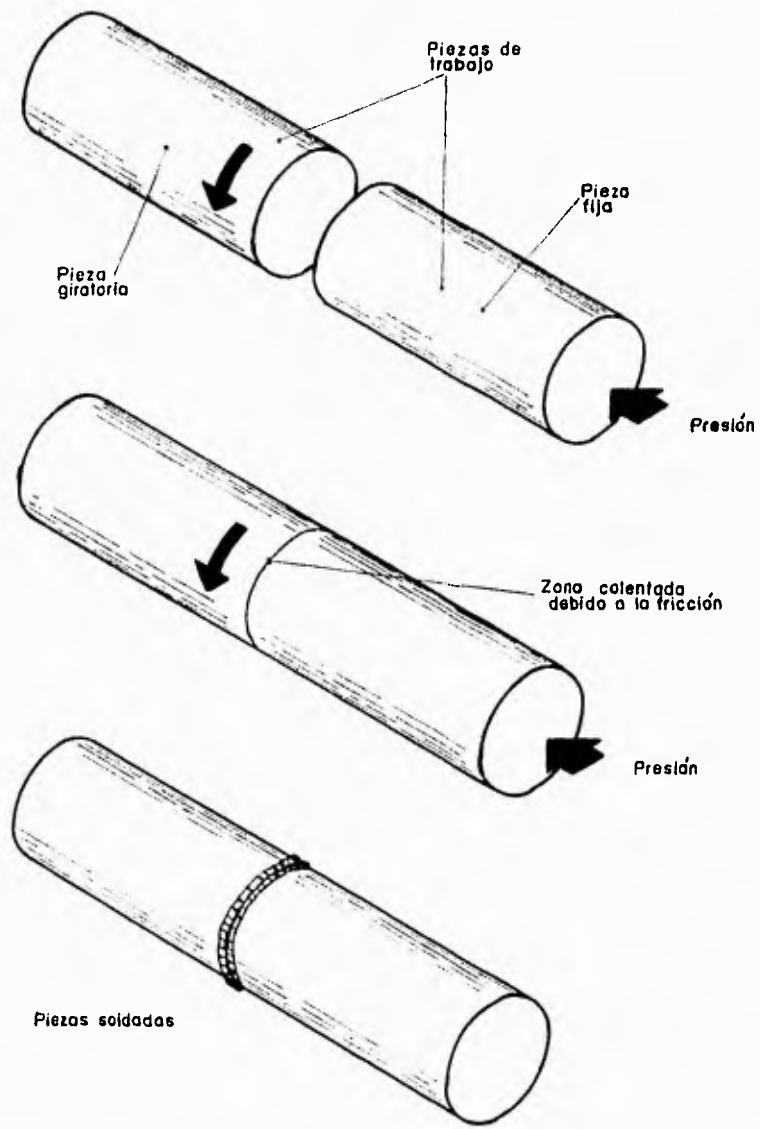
Soldadura por fricción (FRW)
